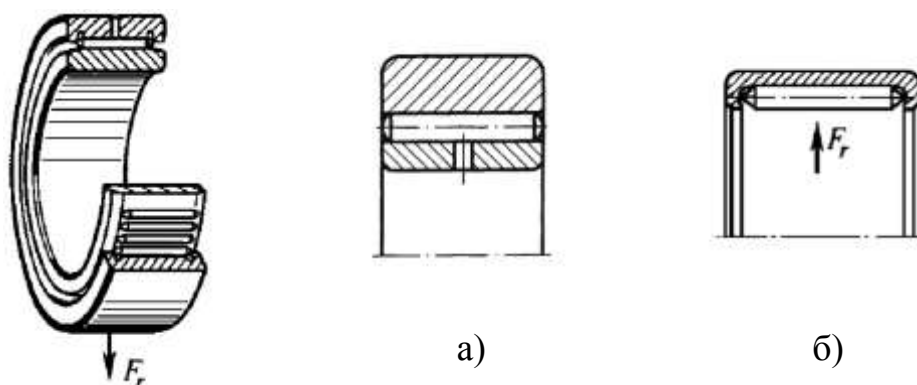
Роликовые радиальные подшипники с игольчатыми роликами
